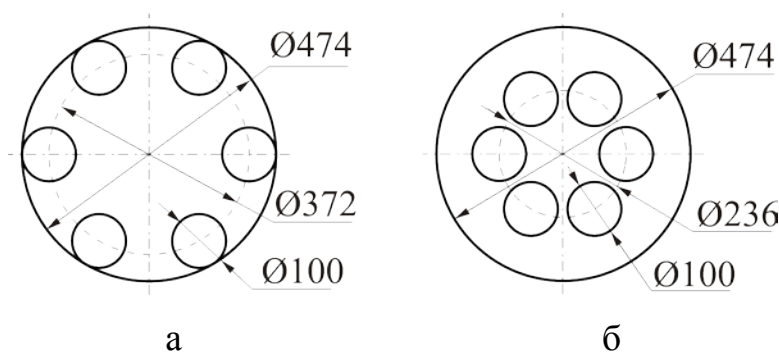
Схема вырезки образцов из колесной заготовки диаметром 474 мм: а- заготовки из периферийной части слитка, б- срединной части
